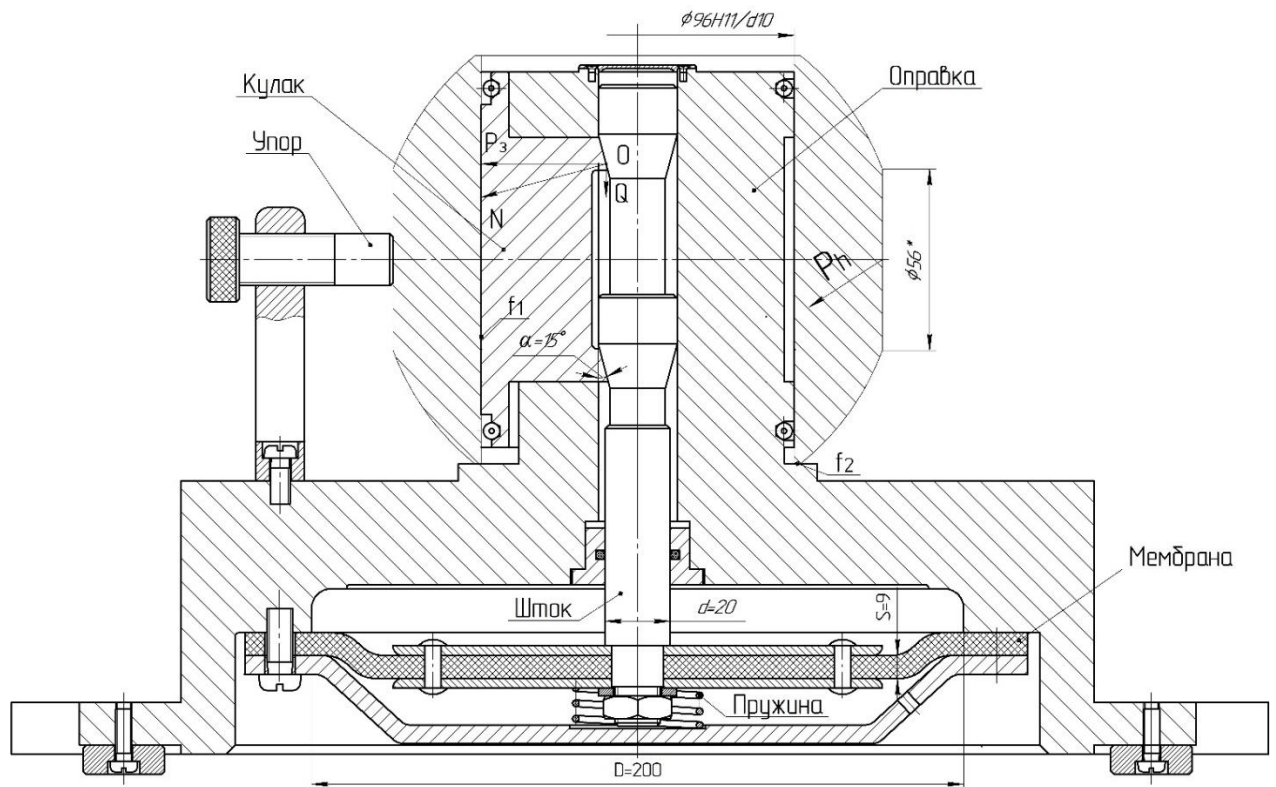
Схема до розрахунку сили закріплення заготовки
